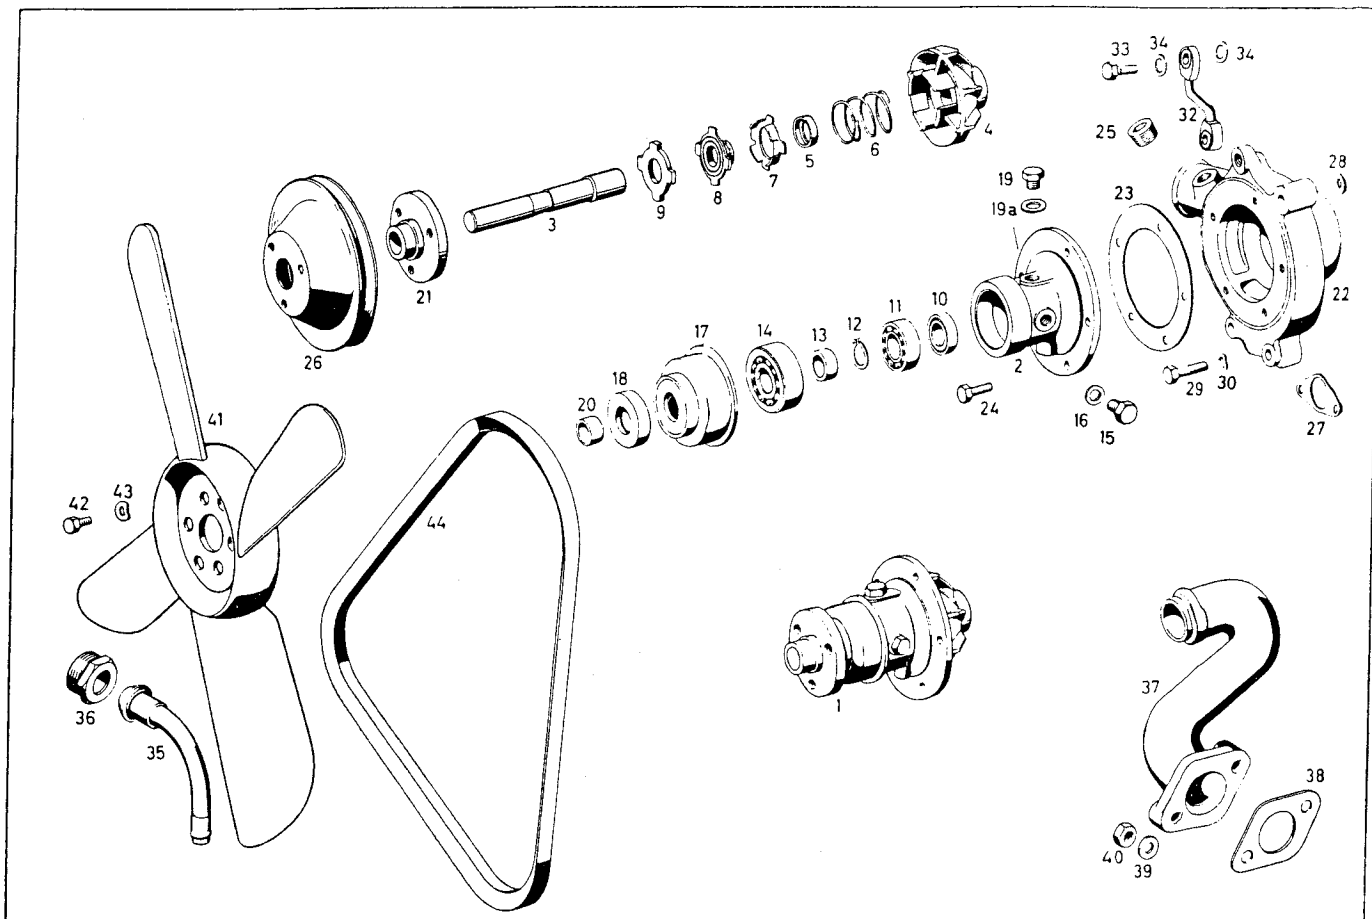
Montagebild der zerlegten Wasserpumpe (OM 636)
